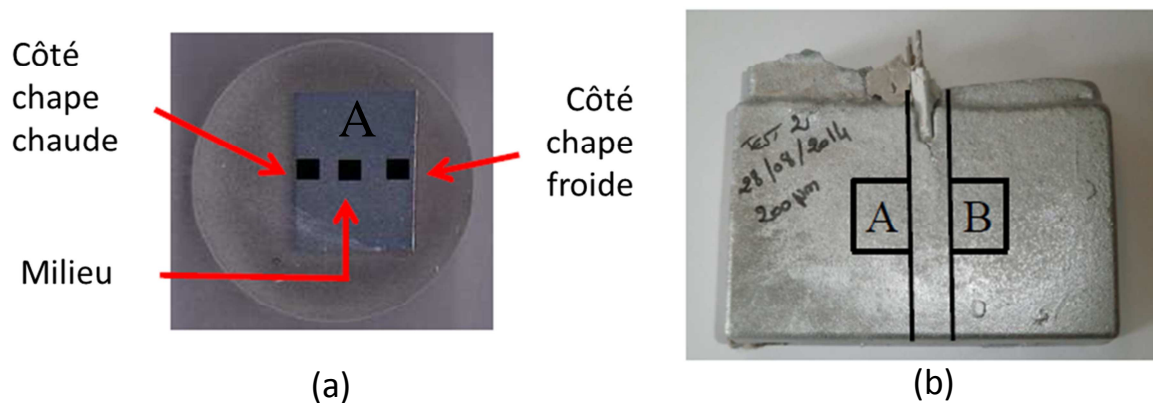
Zones de mesure du SDAS : a) vue en coupe de la pièce moulée, b) vue de face
